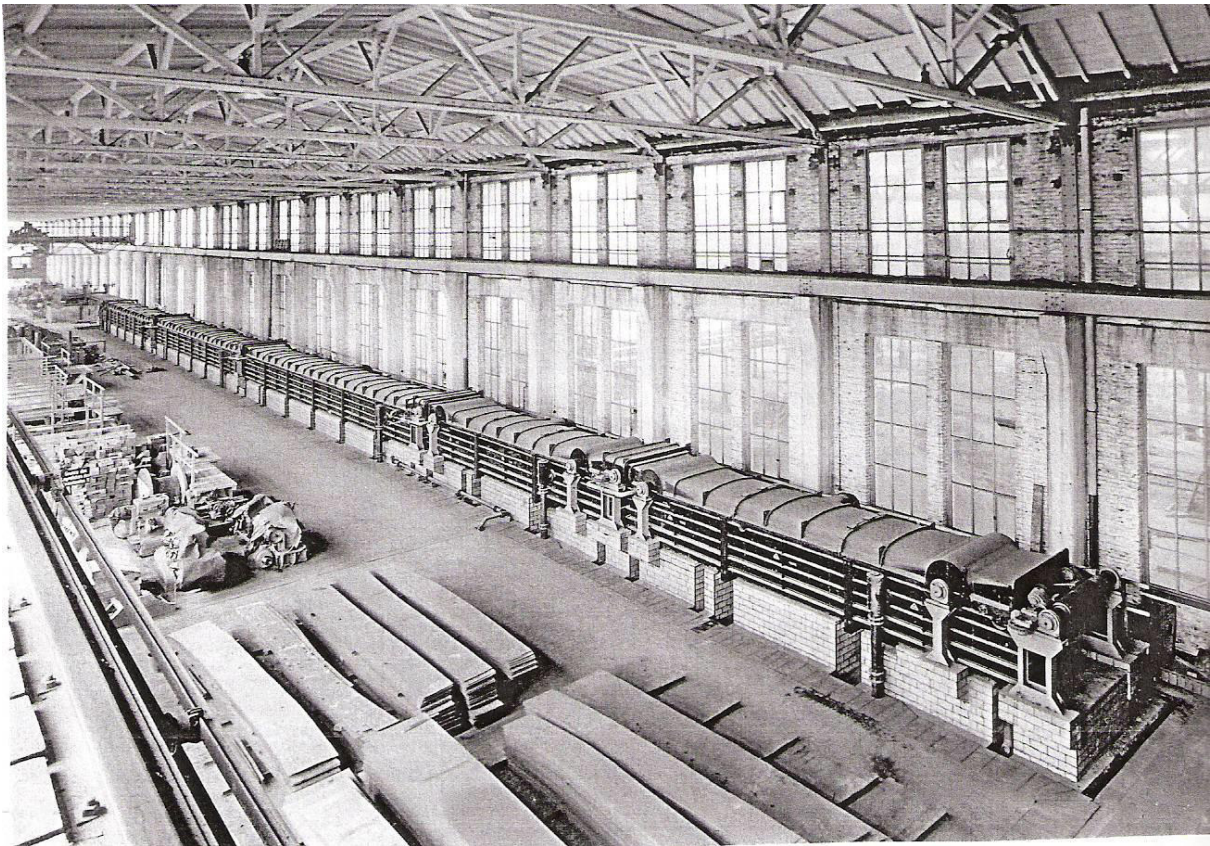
Steckelwalzwerk, Durchlaufbeize
